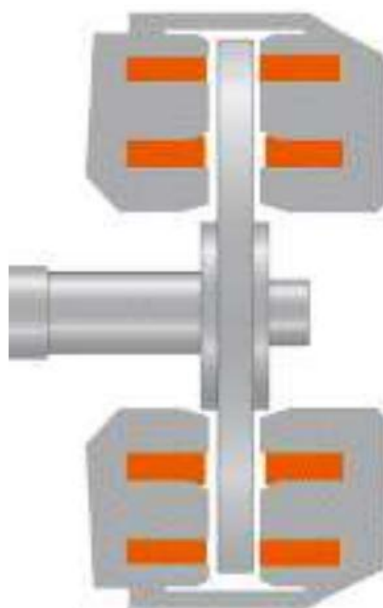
Расположение вала в упорных бесконтактных подшипниках
